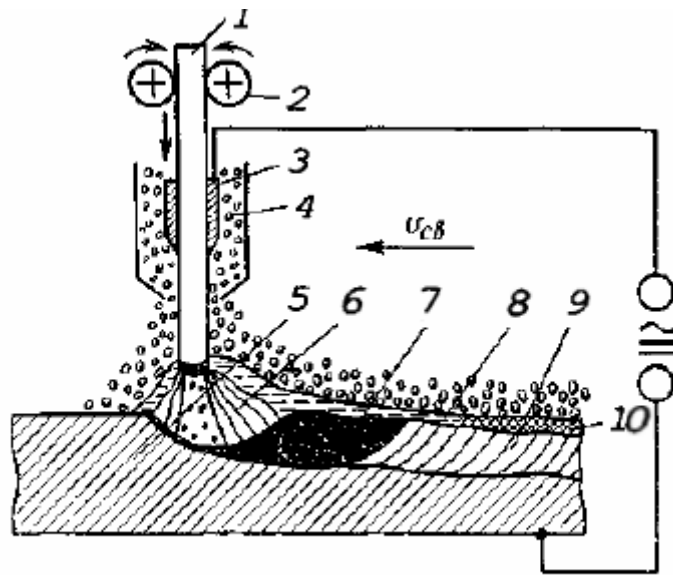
Схема автоматичного зварювання під флюсом:
